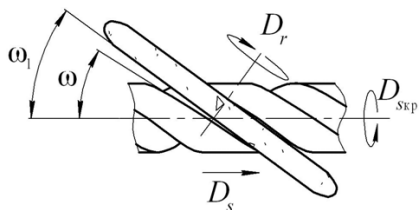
Установка шлифовального круга при вышлифовывании стружечной канавки
